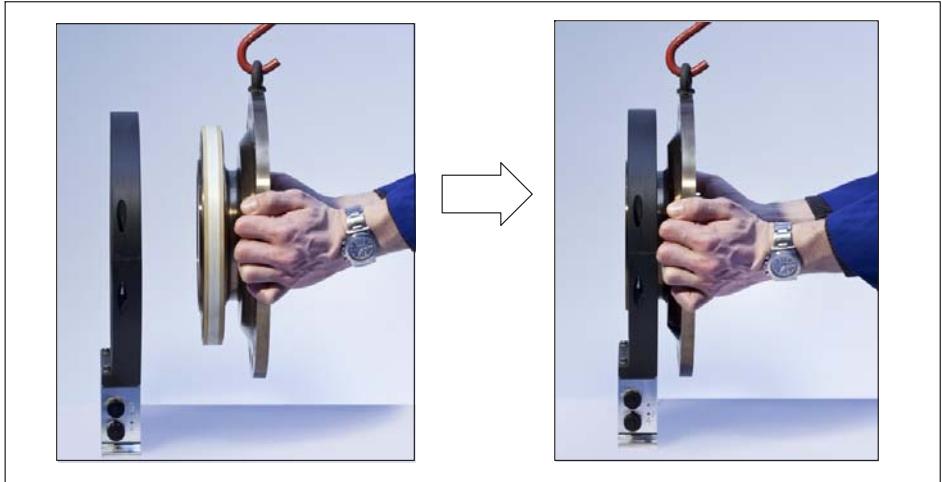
Ausrichten des Rotors mit dem Stator
